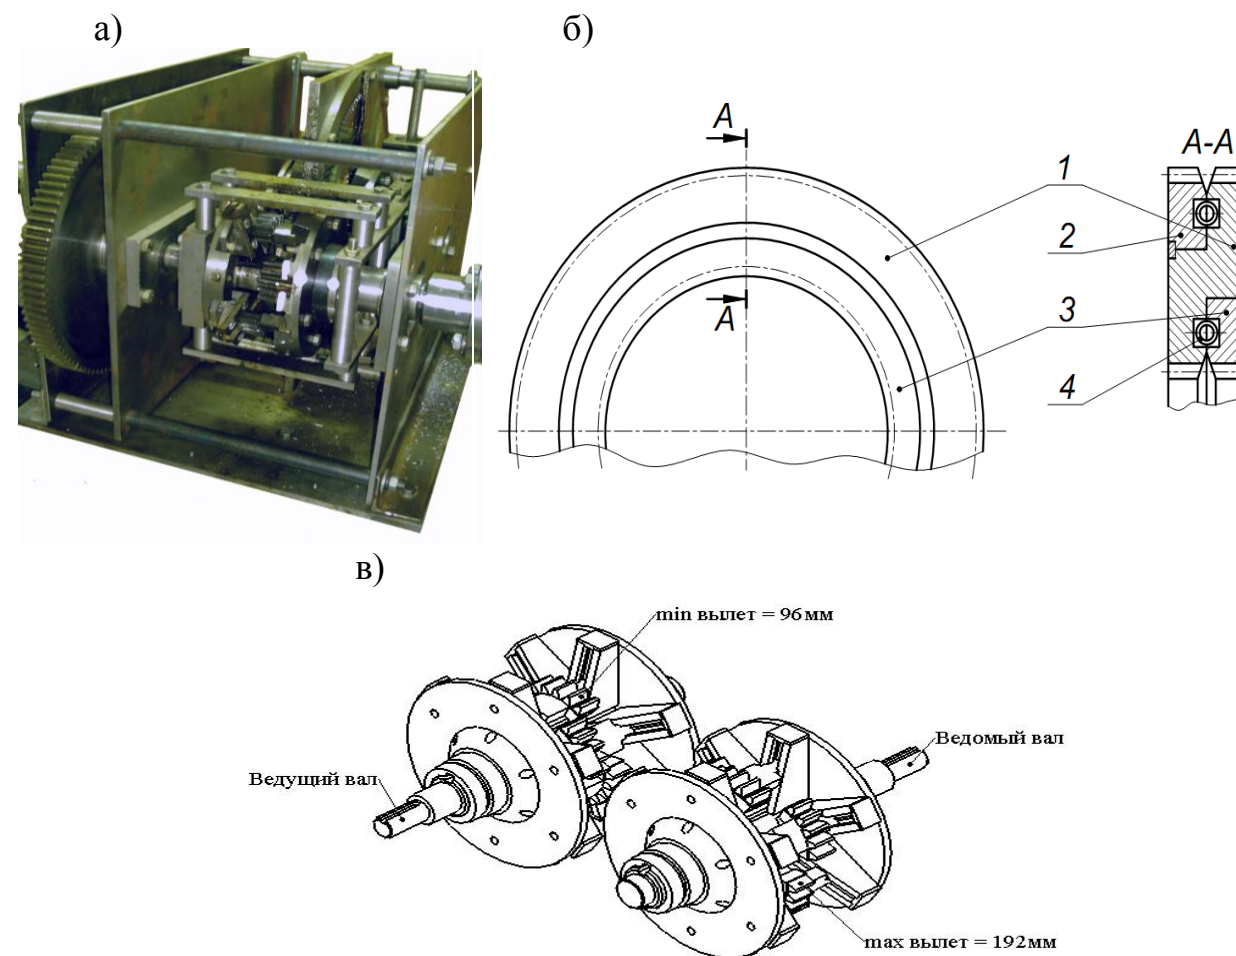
Развернутая зубчатая плавнорегулируемая передача: а – макет передачи; б – центральное зубчатое колесо; в – составные зубчатые колеса
